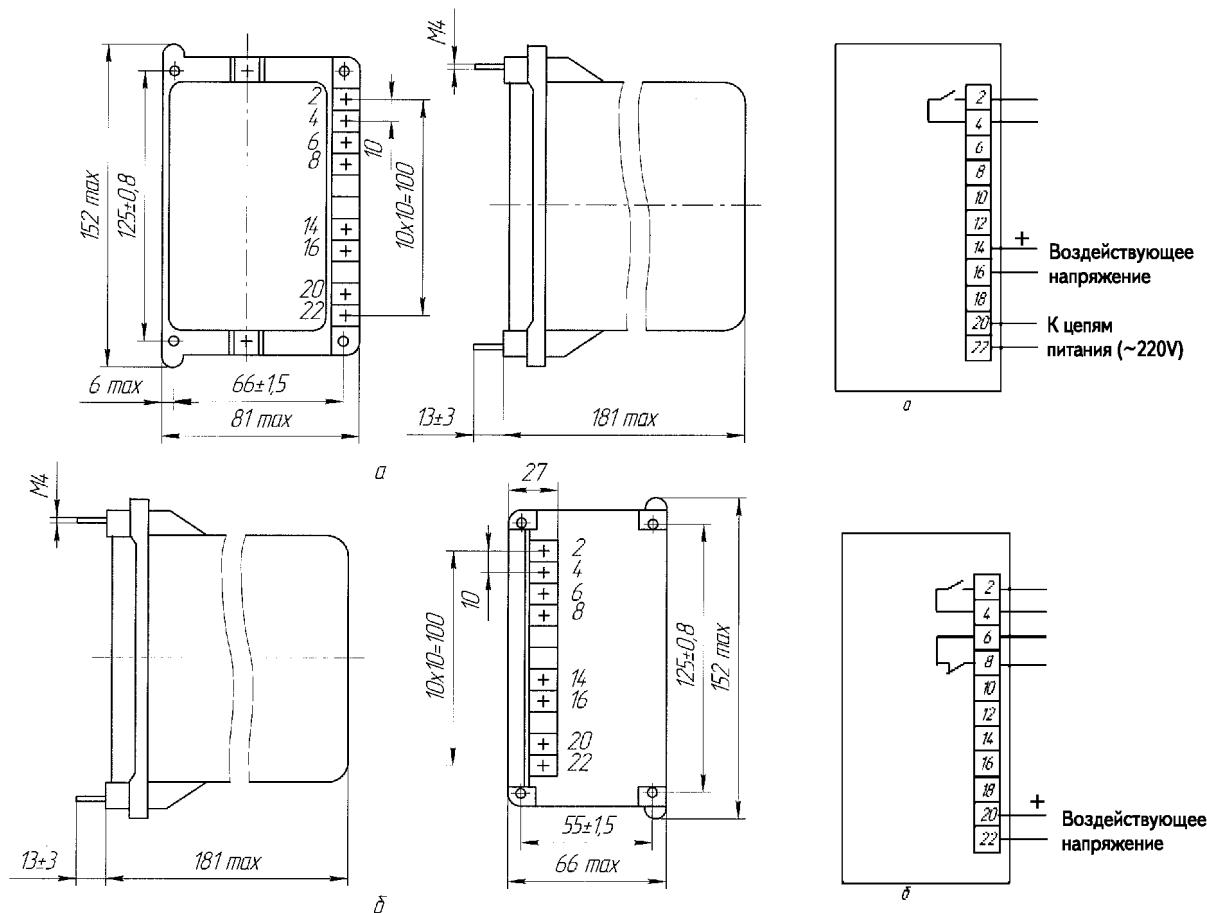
Габаритные, установочные, присоединительные размеры реле РЧН 11, РЧН 12, РЧН 18.
